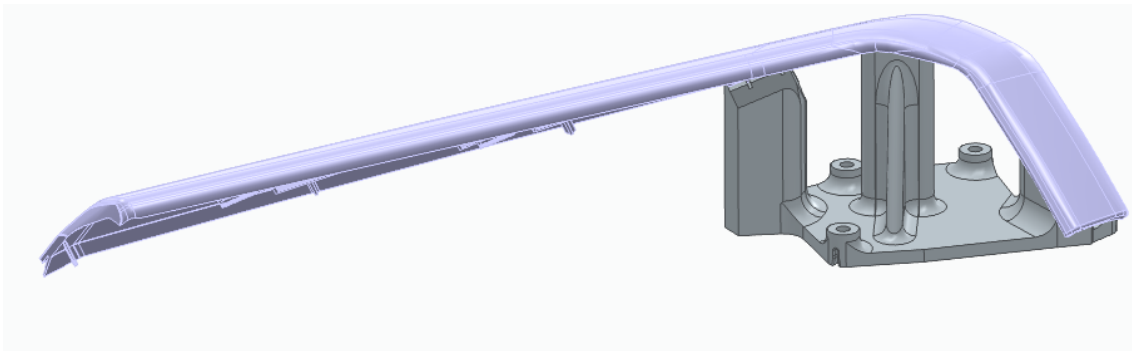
Módulo 2 del utillaje 4 con pieza de trabajo incorporada
